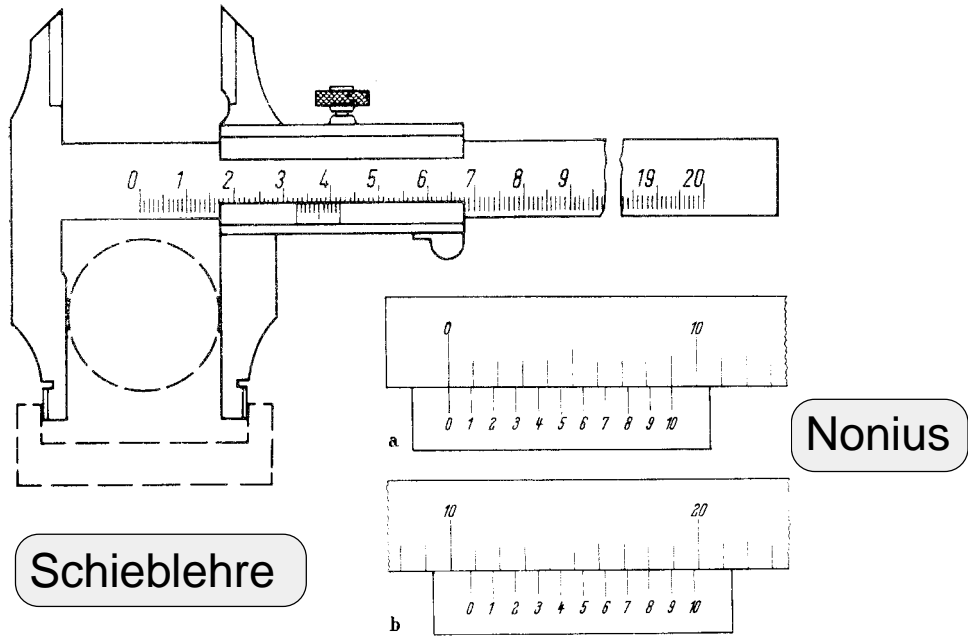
Werkzeuge zur Messung von Längen.
